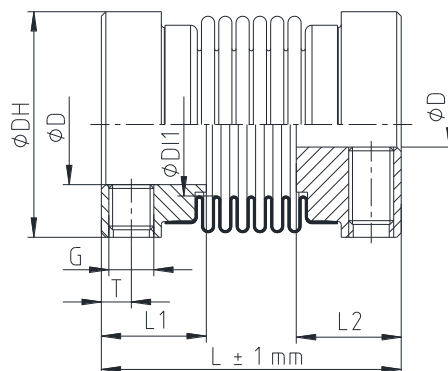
TOOLFLEX® Bauart M mit Gewindestift (Ausf. 1.1)
